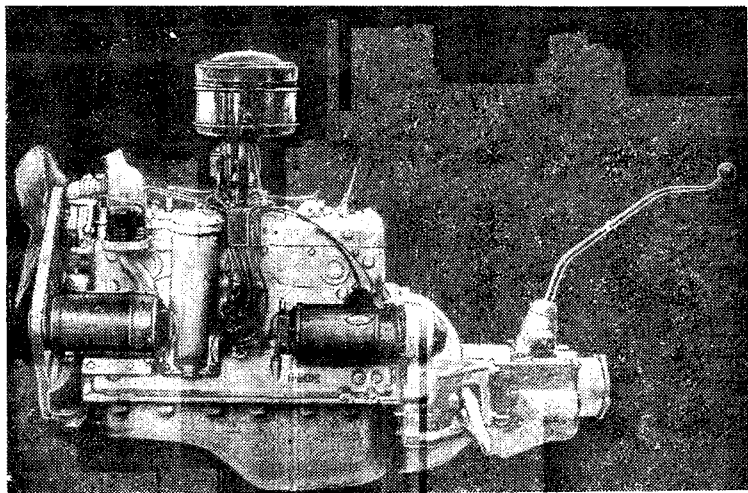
Общий вид шестицилиндрового двигателя со стороны генератора.
